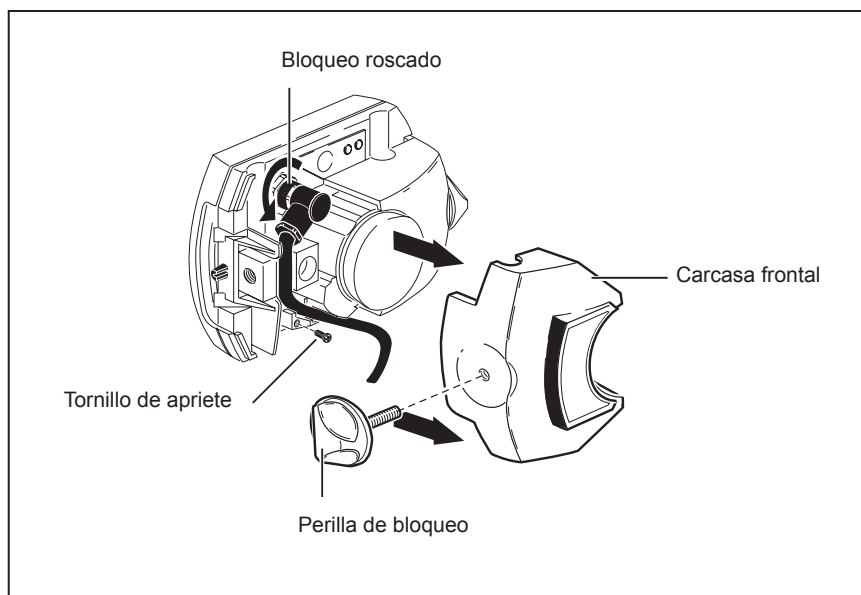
Reemplazo del cable del módulo inalámbrico por el cable del sensor
